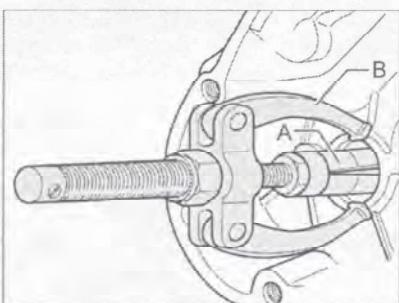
Извлечение роликоподшипника вторичного вала.
